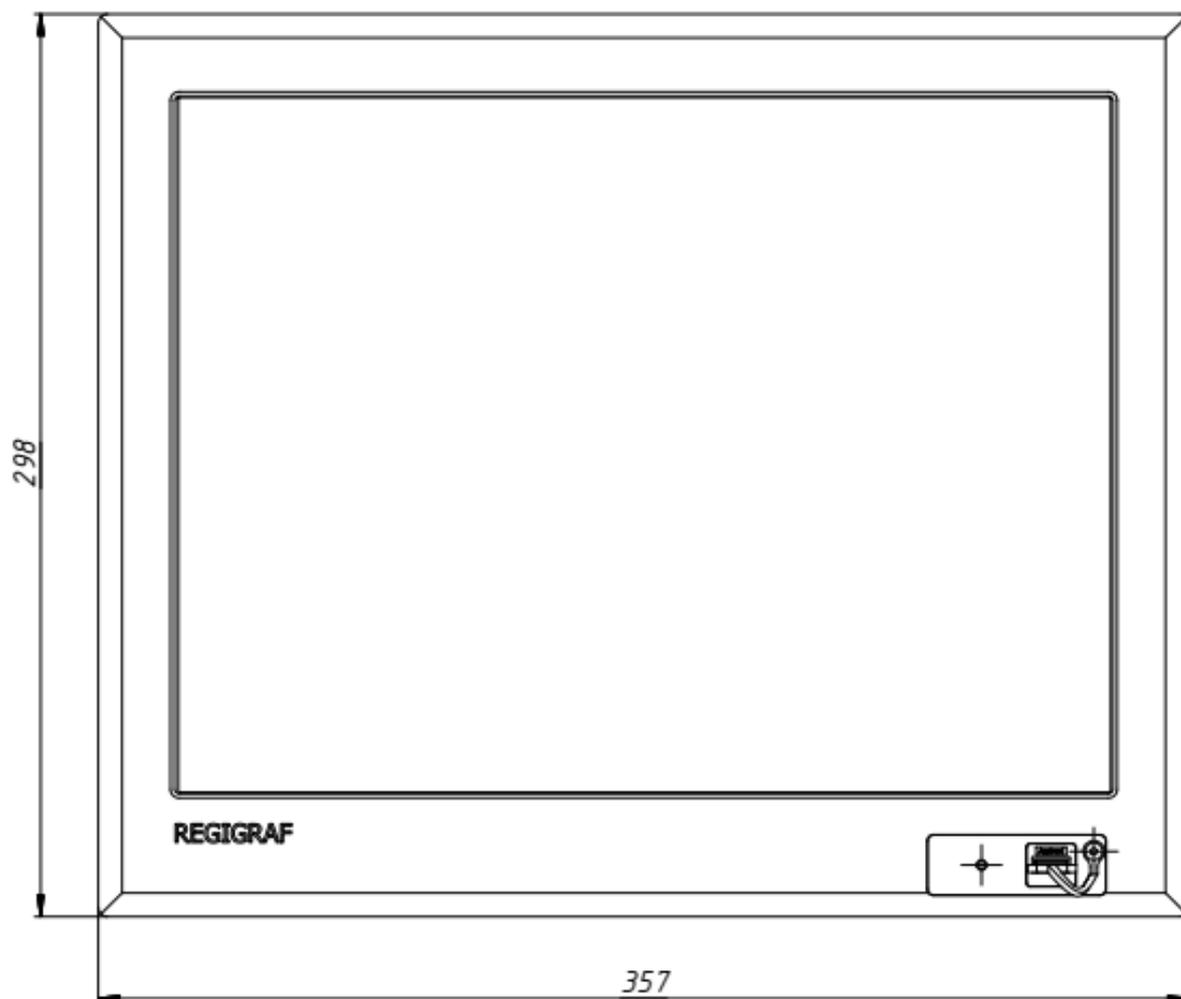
Габаритный чертёж прибора в исполнении Ф1772–3, вид спереди
